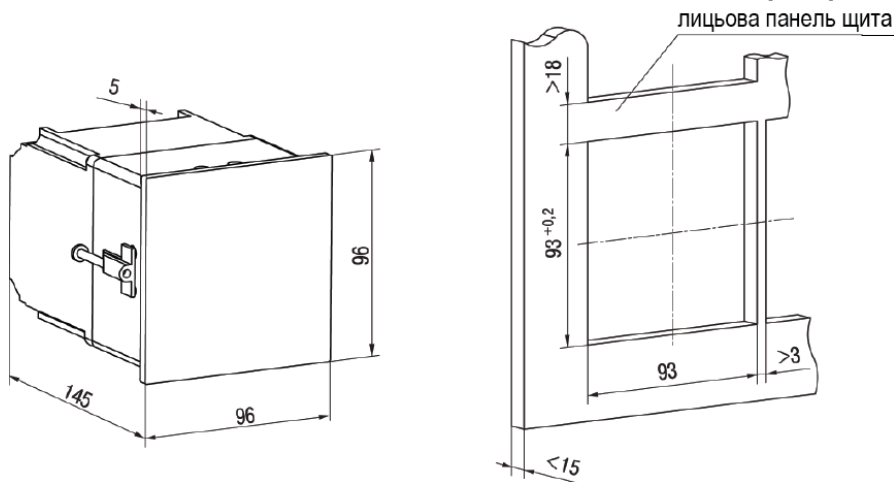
Габаритні розміри корпусу Щ4
